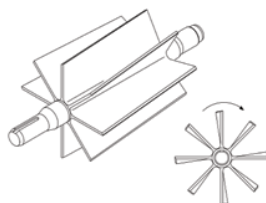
Rotor s redukovanou kapacitou [22]
